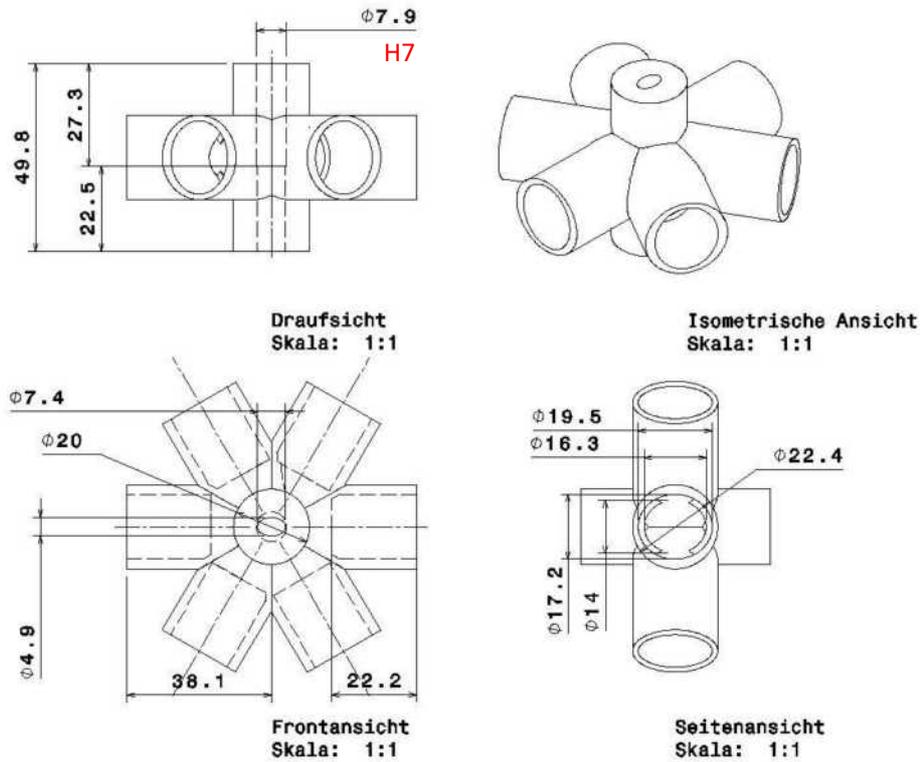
Element 1 (2D-Zeichnung) mit Toleranz Toleranz: mittel.
